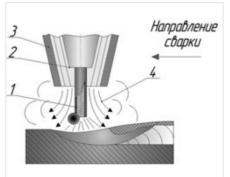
Схема процесса сварки порошковой проволокой в защитном газе.
